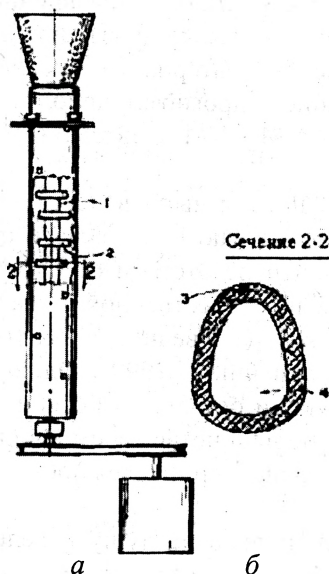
Установка для ЦЛ распредвала из КМ; а – общая схема установки, б – поперечное сечение отливки.
